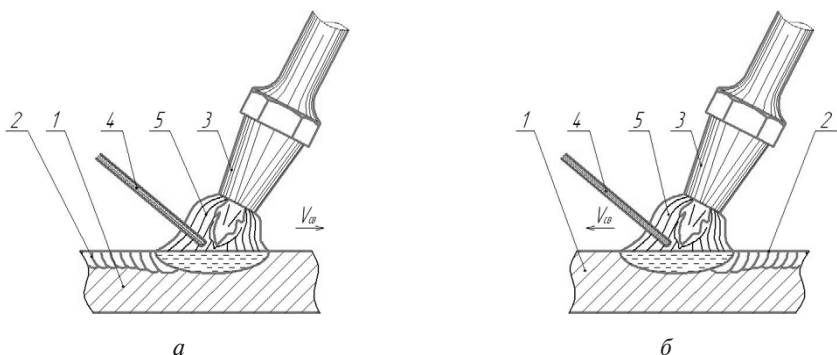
Схемы основных способов газовой сварки:
